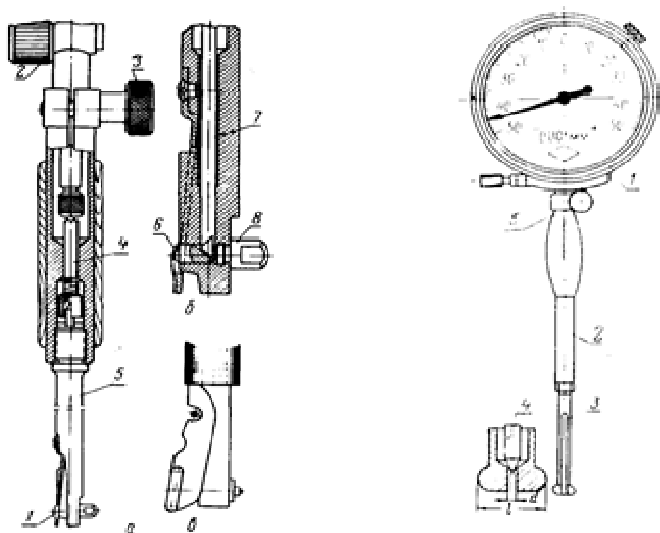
Индикаторный нутромер с клиновой передачей: 1 – центрирующий мостик; 2 – индикатор; 3 – стопорный винт; 4 – движок; 5 – трубка; 6 – подвижный стержень с клиновым срезом; 7 – шток с клиновым срезом в нижней части; 8 – переставной стержень
